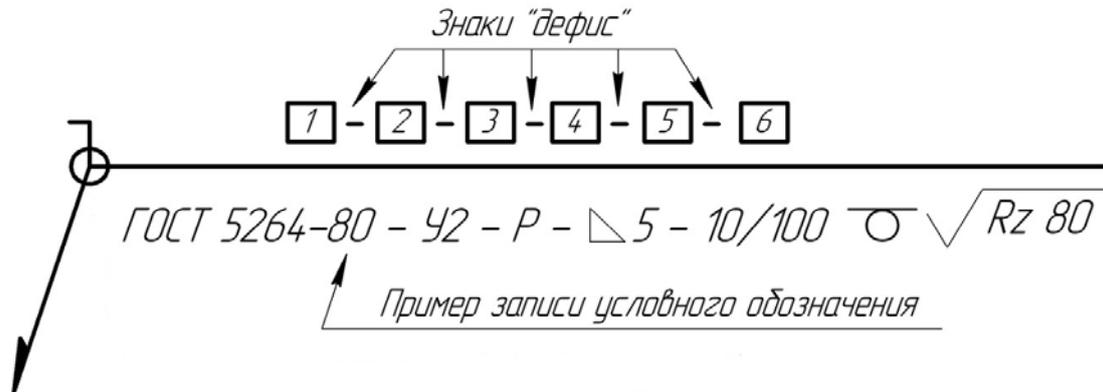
Структура условного обозначения сварного шва
